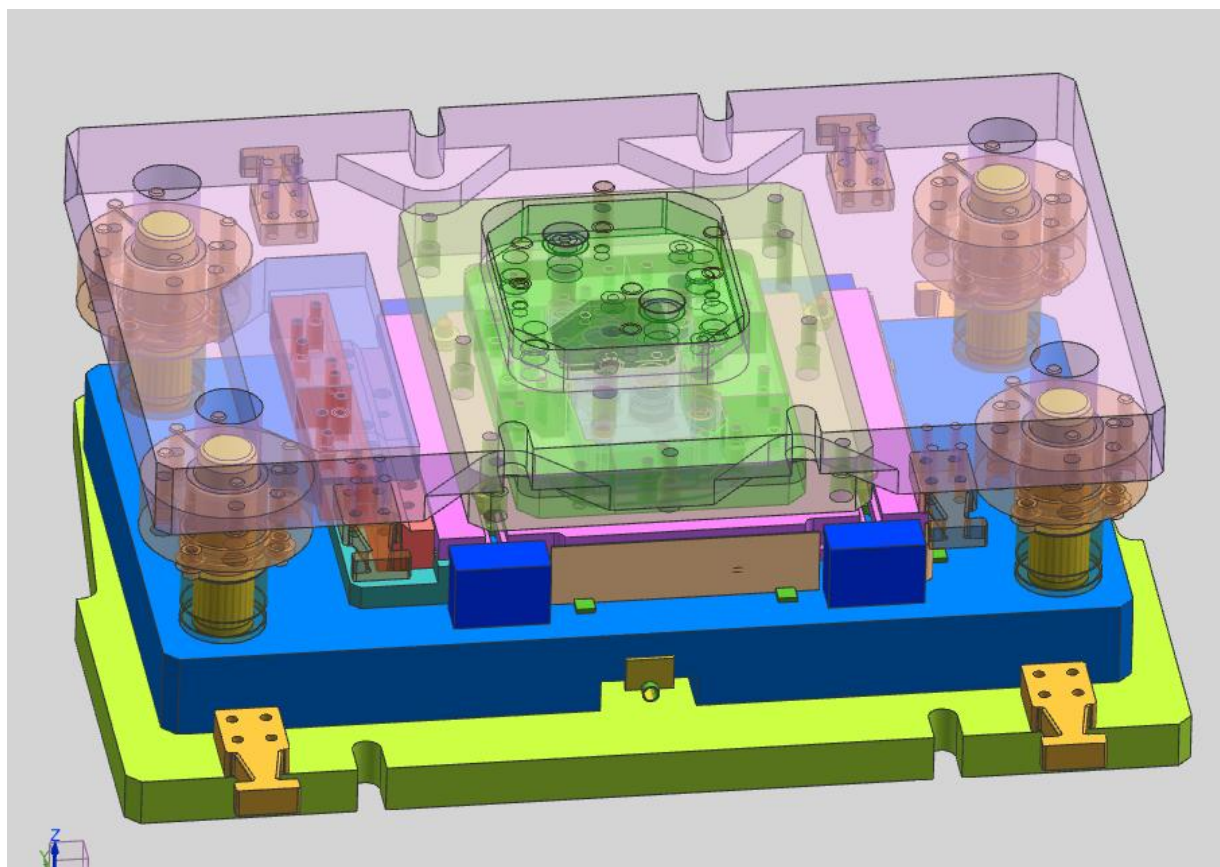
Штамп для вырубки-пробивки
